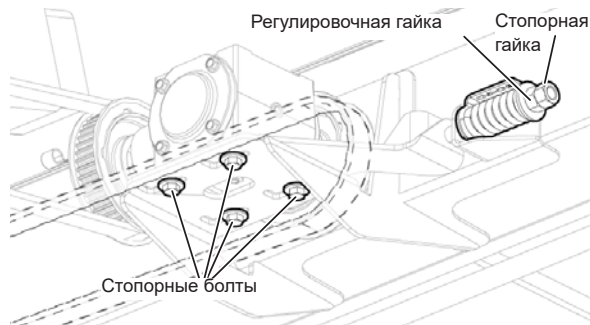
Регулировка натяжения второго ремня правого полотенного транспортера.
